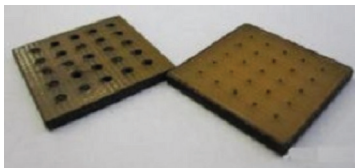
Технологические пробы деталей из гетинакса, изготовленные резкой лазером.
